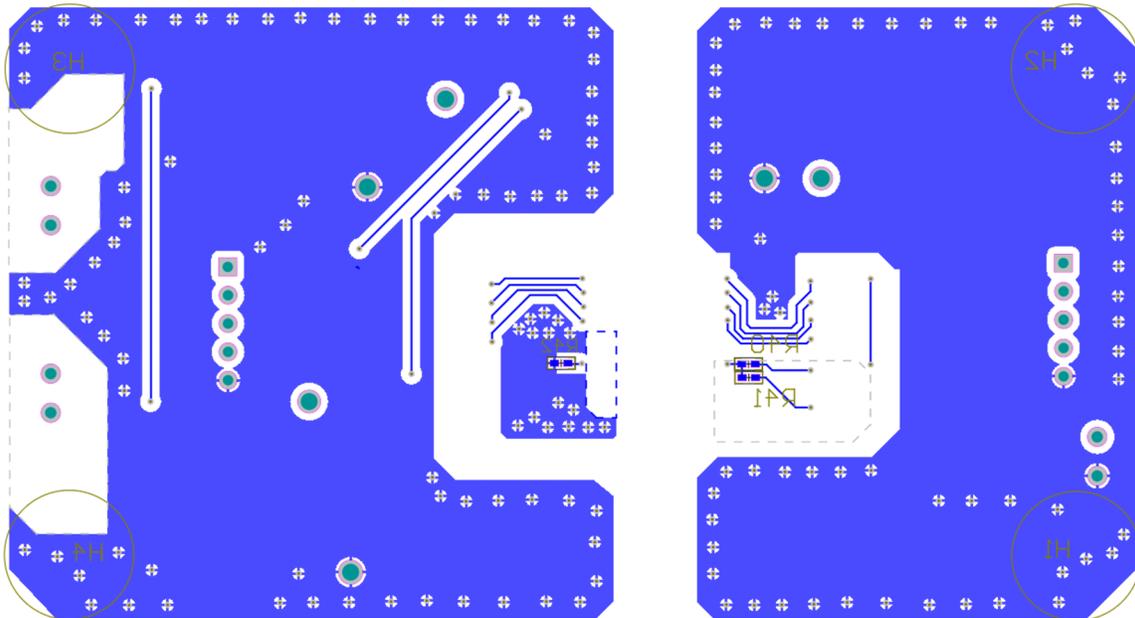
ISOW7741DFMEVM PCB 布局 - 底层
